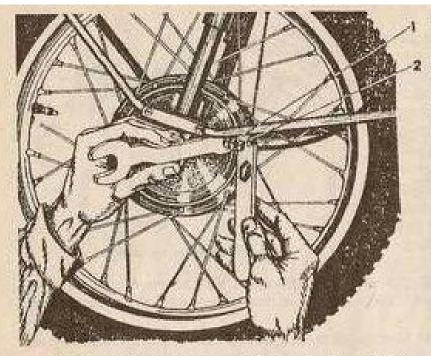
Регулировка тормоза переднего колеса: 1 — гайка, 2 — упор
